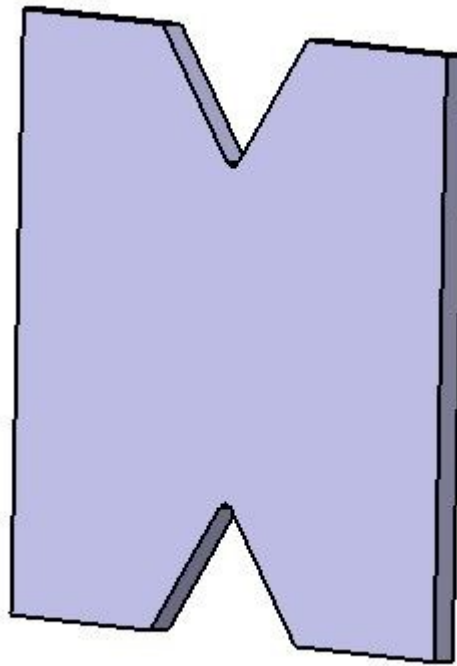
Model zkušební vzorku pro tlakovou zkoušku laminátu z tkaniny
